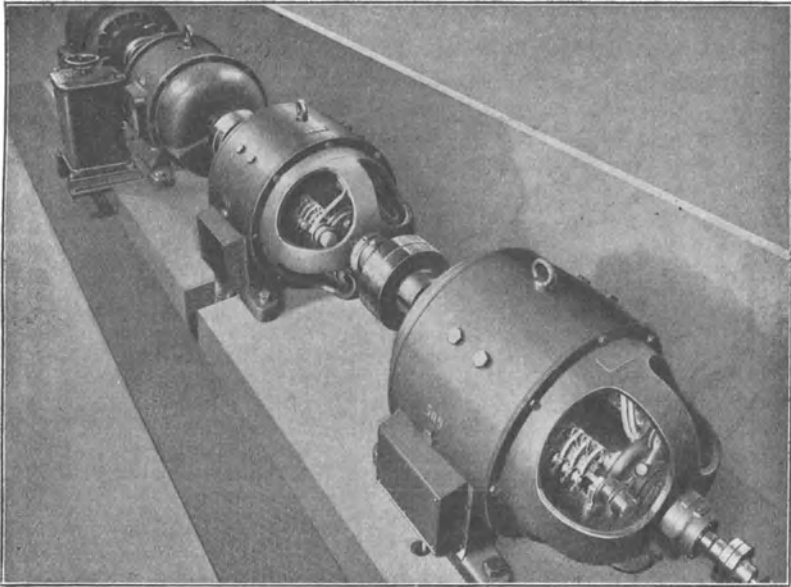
Mehrfachschweißumformer für Gleichstrom.
